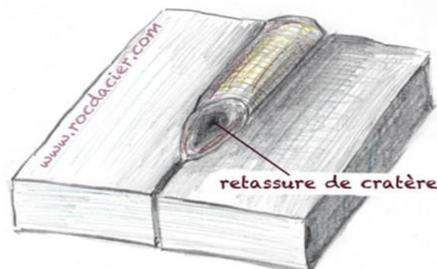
Défaut de soudure soufflure et cavité.
